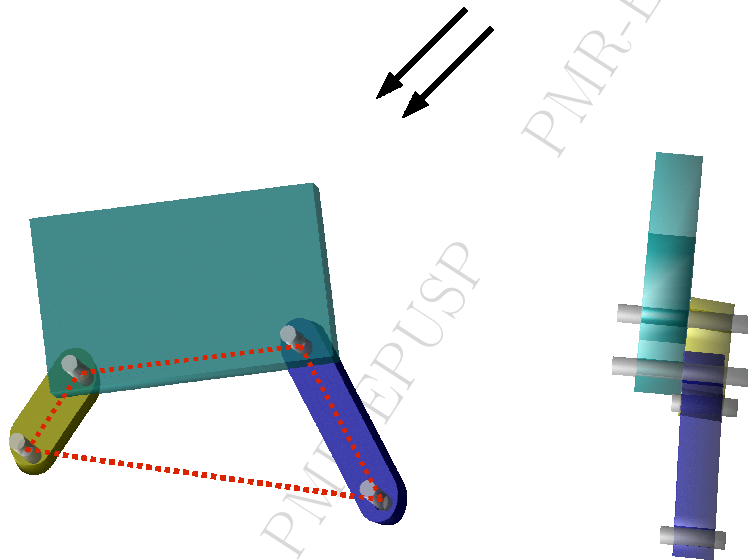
Mecanismo plano de 4 barras tipo RRRR.
